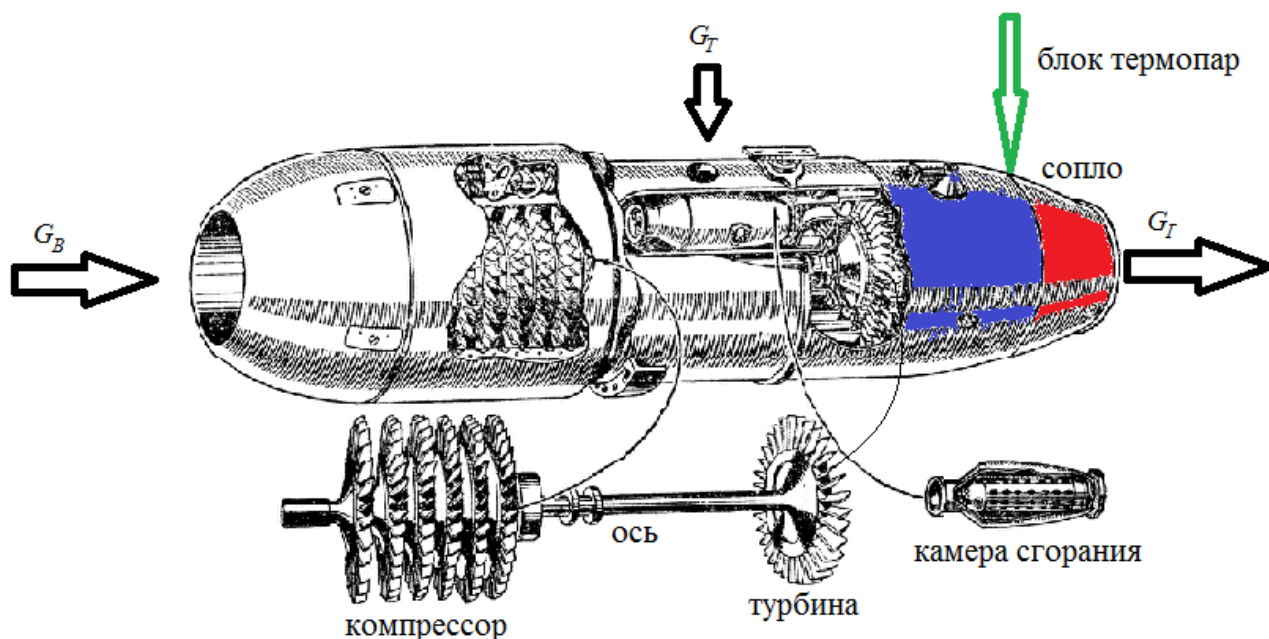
Схема типовой установки блока термопар в ГТД
